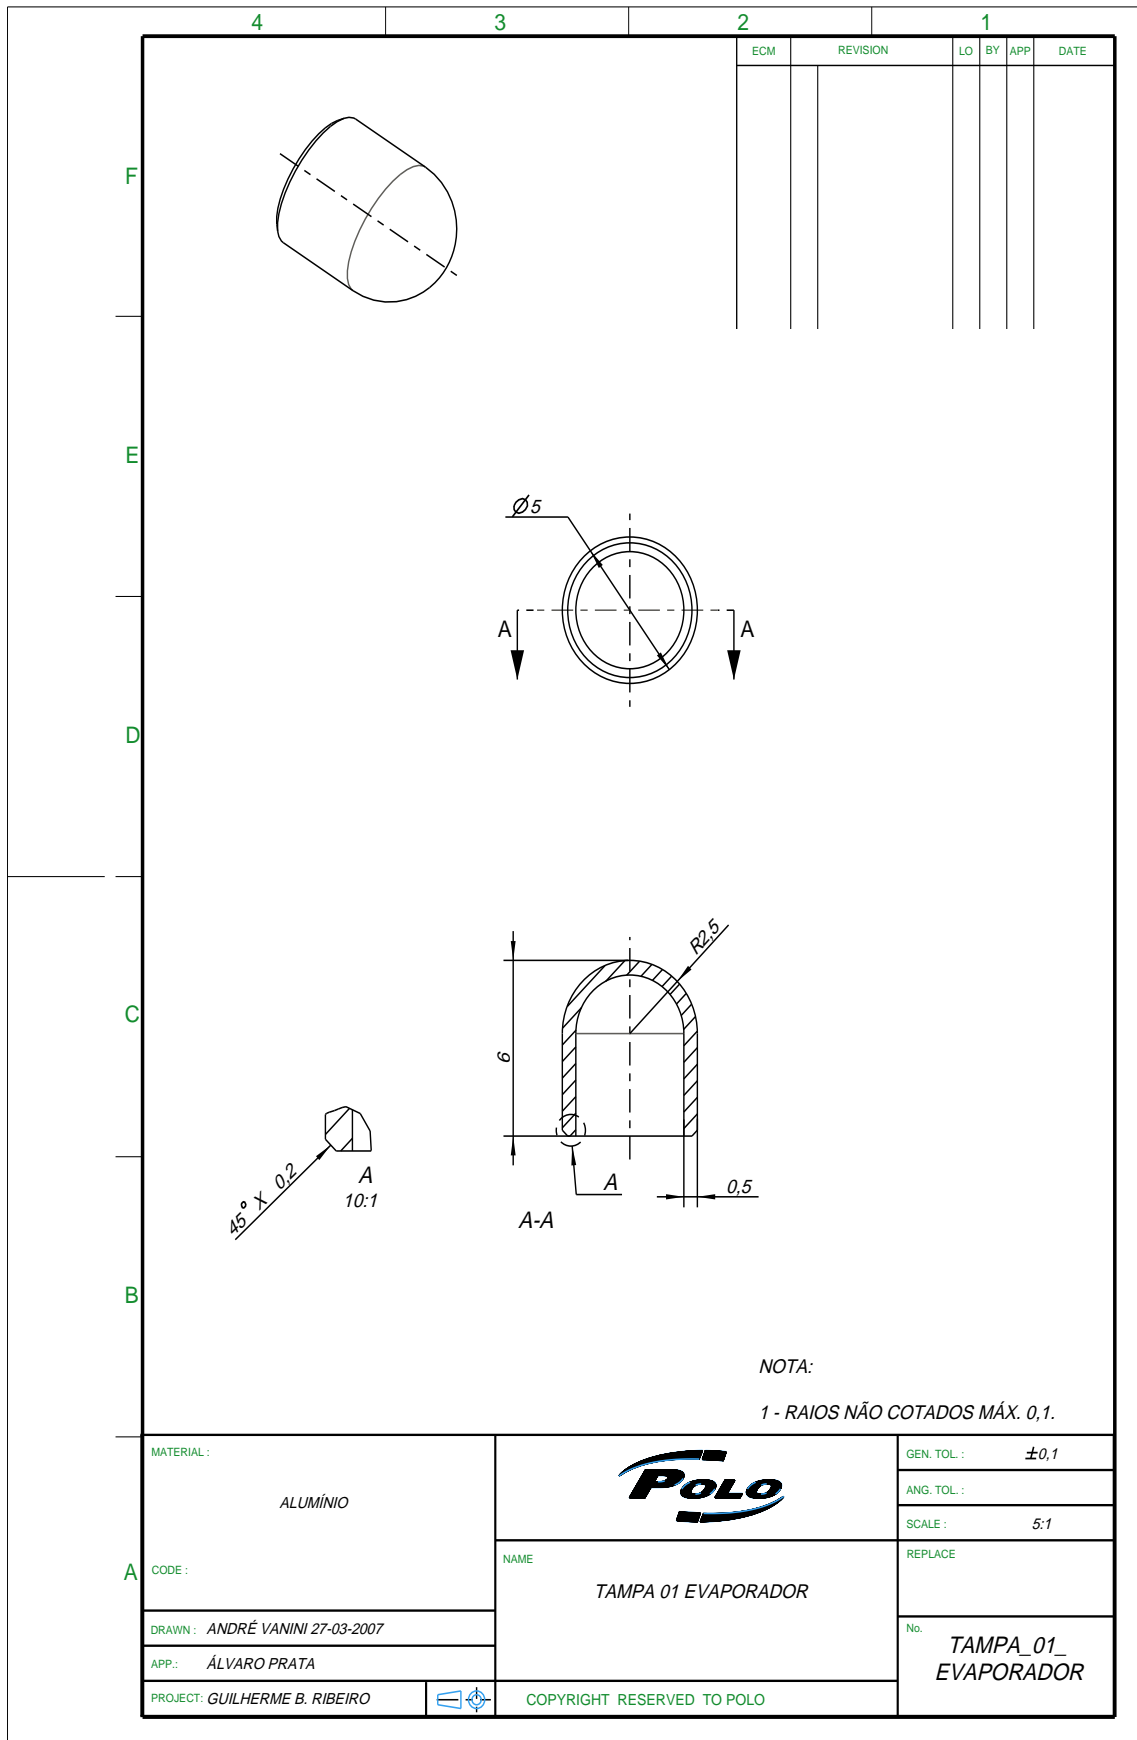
Desenho técnico do evaporador acoplado a tubos de calor - Parte V
